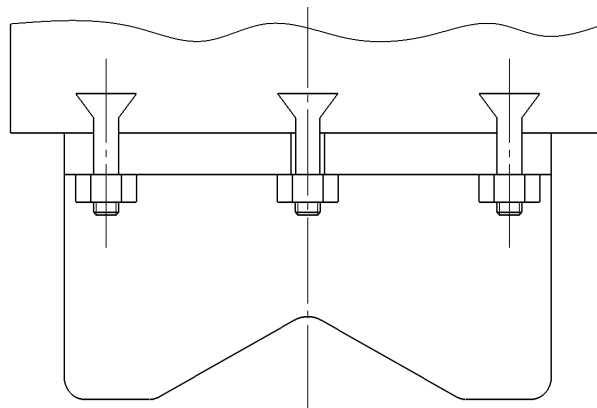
Эскиз вырезного ковочного бойка с болтовым креплением
